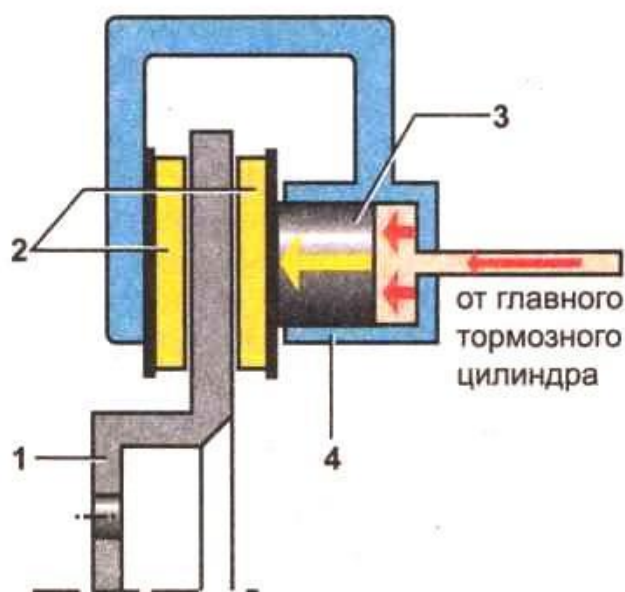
Принцип работы тормозного механизма с плавающей скобой 1 – тормозной диск; 2 – тормозные колодки; 3 – поршень; 4 – рабочий тормозной цилиндр (суппорт)
